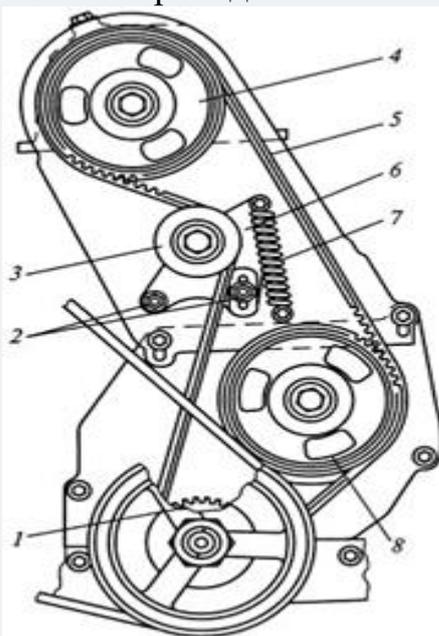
Ременный привод распределительного вала: 1, 4, 8 – шкивы; 2 – болты; 3 – ролик; 5 – ремень; 6 – кронштейн; 7 – пружина
